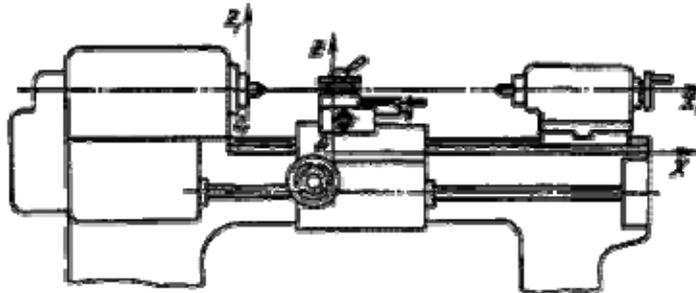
Система прямоугольных координат токарно-винторезного станка
